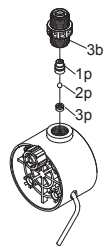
Подпружиненный клапан DN 4 / подпружиненный клапан DN 8
